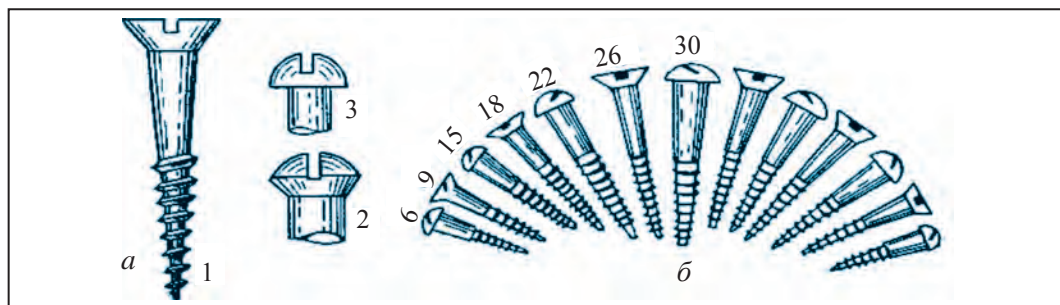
Шурупы: *а)* головки шурупов: 1 – скрытые; 2 – полускрытые; 3 – полукруглые; *б)* размеры шурупов.
